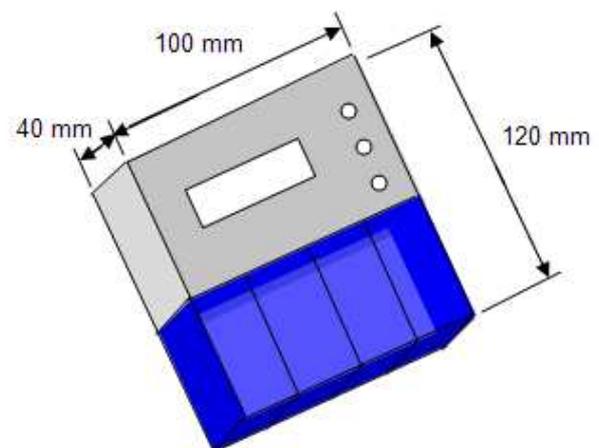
Perspectiva isométrica com as dimensões do protótipo
